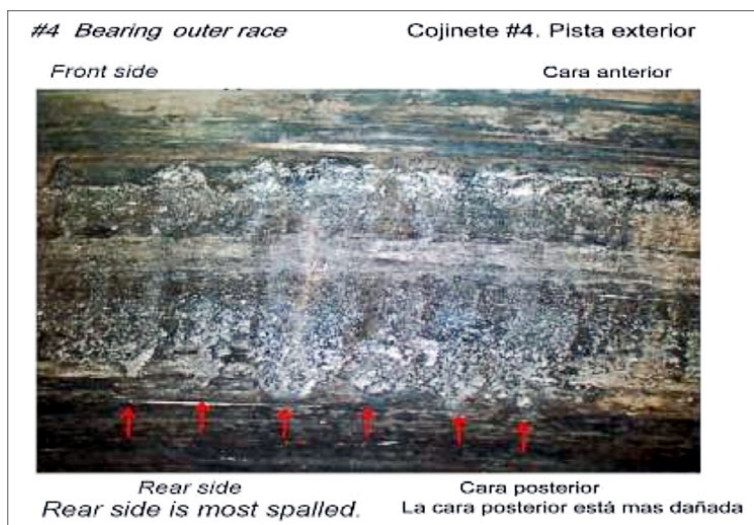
Spalling. Pista exterior del cojinete #4
